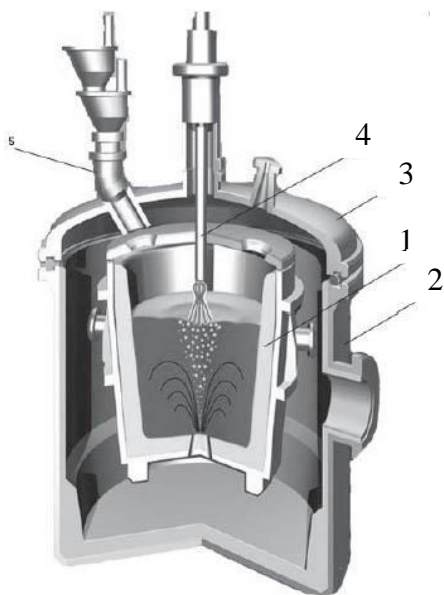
Общая схема камерного вакууматора VD/VOD:
